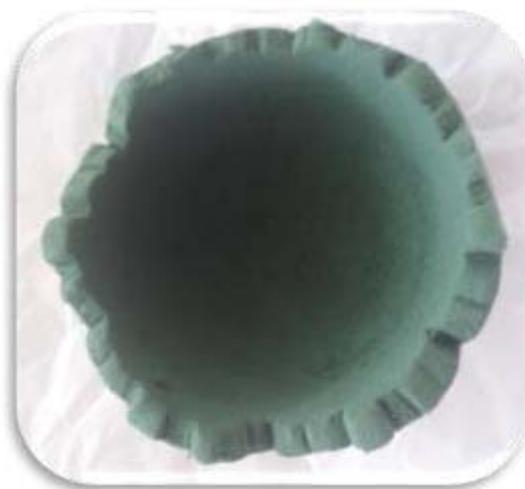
Moldeo de Tapa de azucarera para cortar modulo
